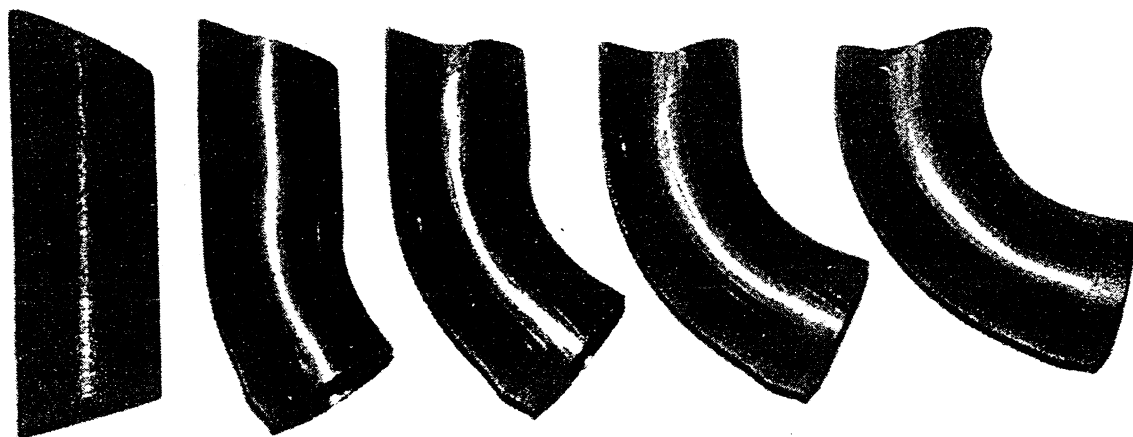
Поетапне деформування заготовки коліна  $90^{\circ}45 \times 2,5$  (сталь 20)
